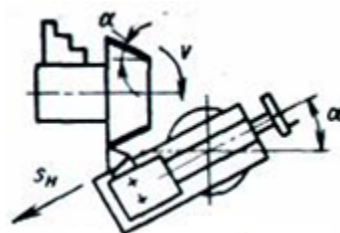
Обтачивание наружных конических поверхностей поворотом каретки верхнего суппорта
